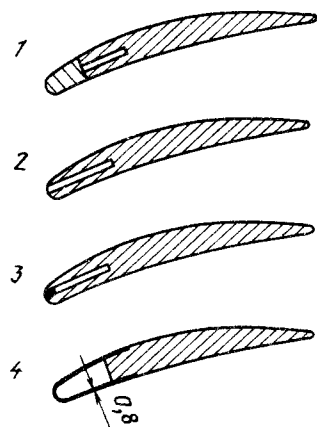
Лопатки входного направляющего аппарата с обогреваемыми входными кромками: 1 — лопатка с приваренным носком и щелью в теле профиля; 2 — лопатка с заваренным концом щели; 3 — лопатка с заделкой конца щели пайкой; 4 — лопатка с накладным носком, приваренным или приклепанным
